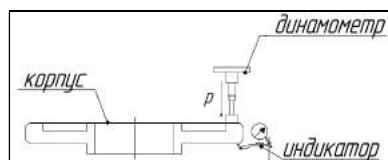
Схема исследования жесткости корпуса фрезы
